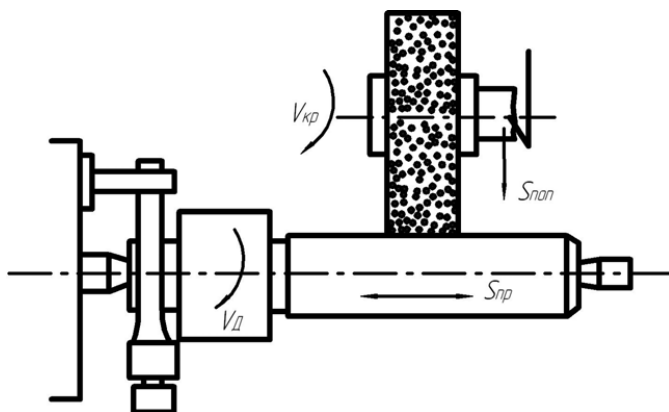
Схема круглого шлифования цилиндрической поверхности
